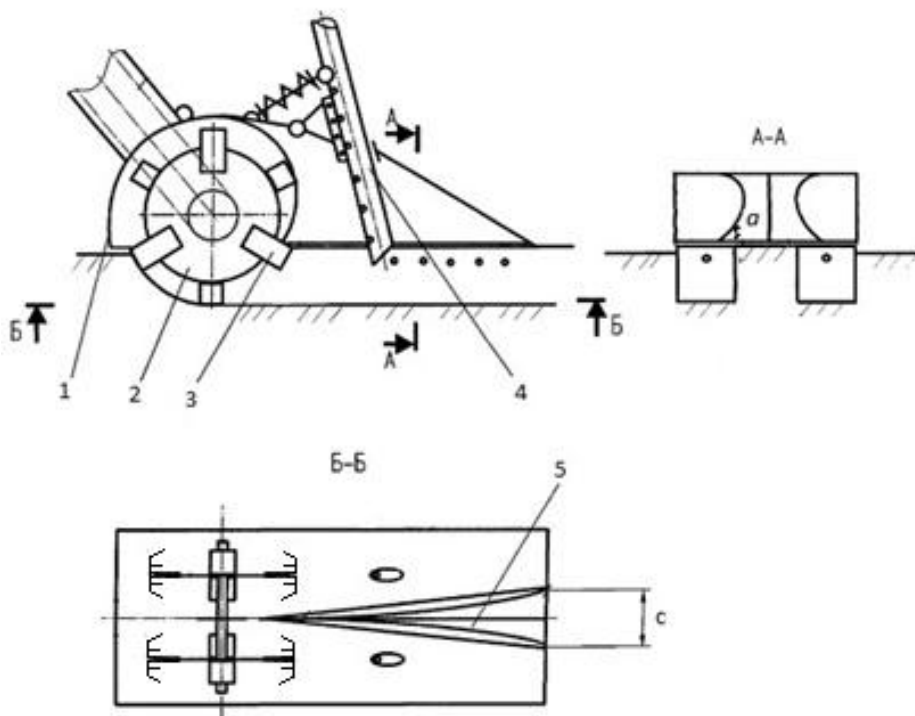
Усовершенствованный фрезерный сошник сеялки СДК-2.8:
